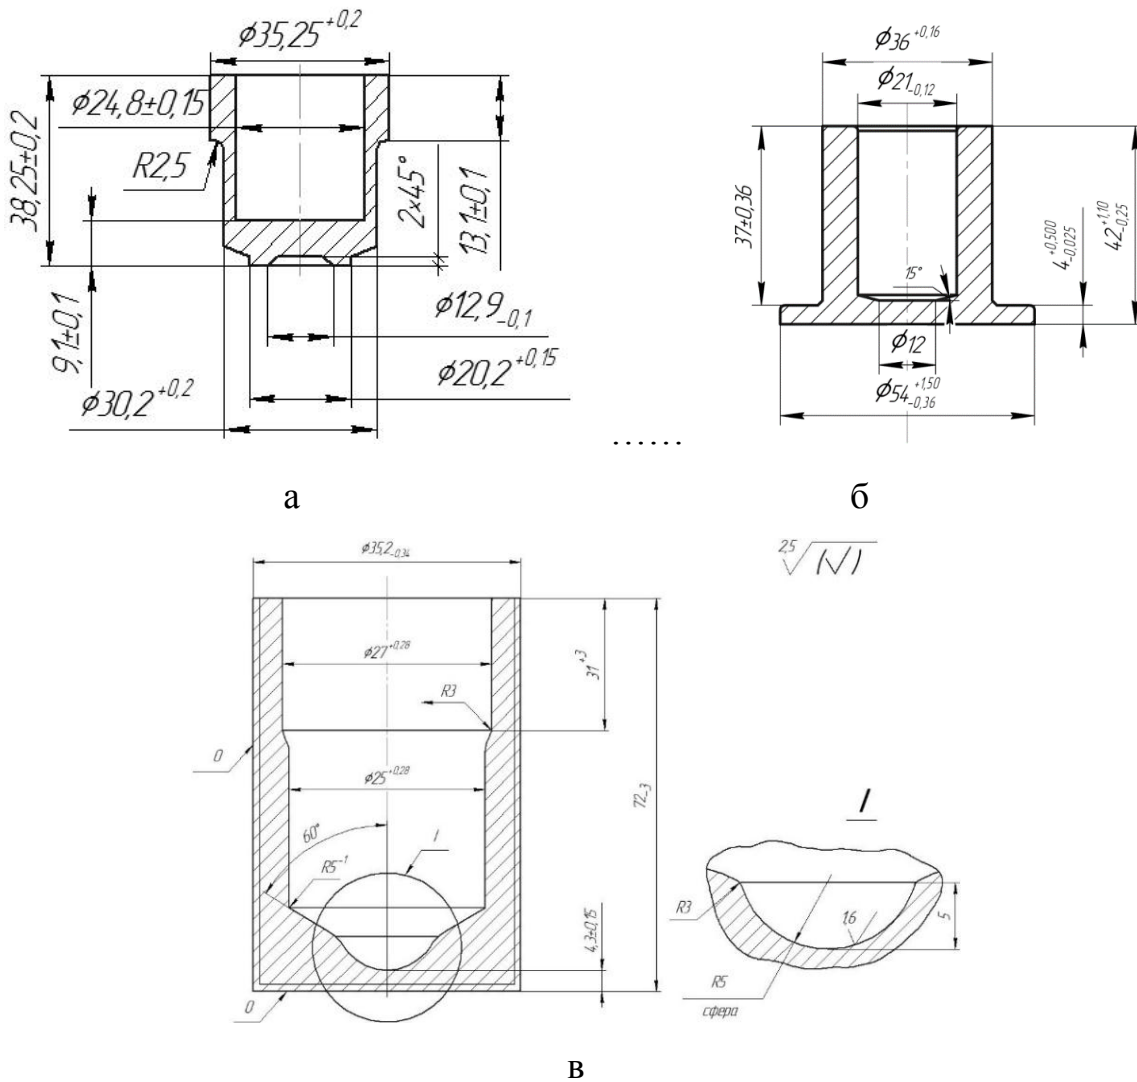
Креслення деталей: корпус (а), стакан (б) і штовхач клапана (б)
